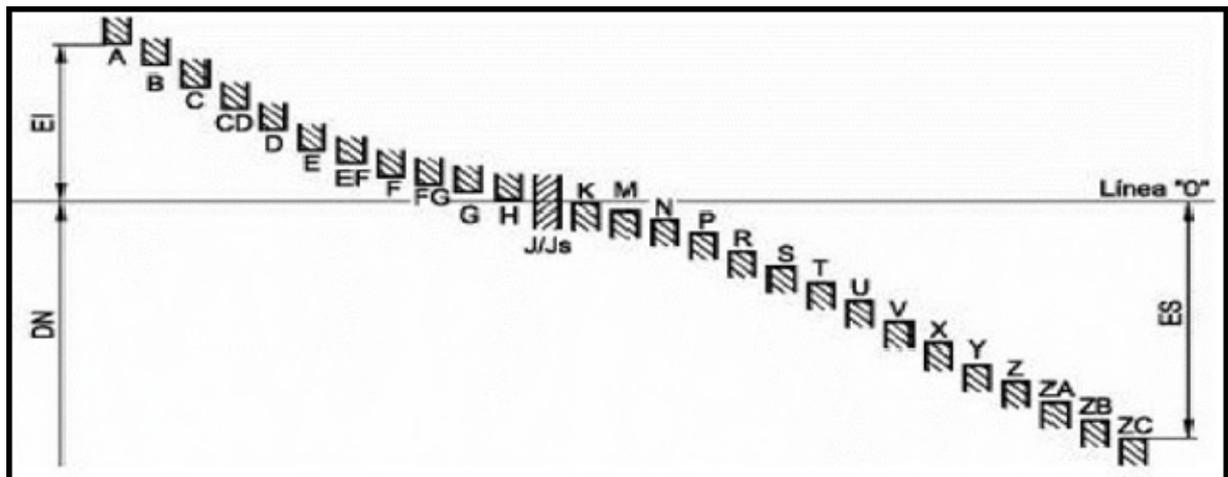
Posiciones de las tolerancias para agujeros
